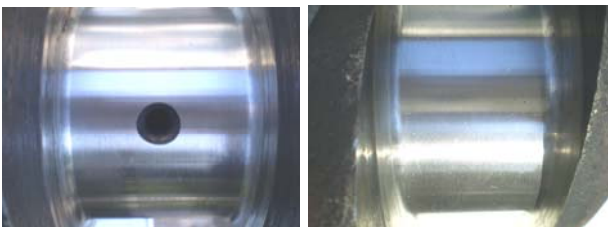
Загальний вигляд робочої поверхні корінної та шатунної шийки сталевого колінчастого валу двигуна 4ЧН 12/14 до зміцнення:
